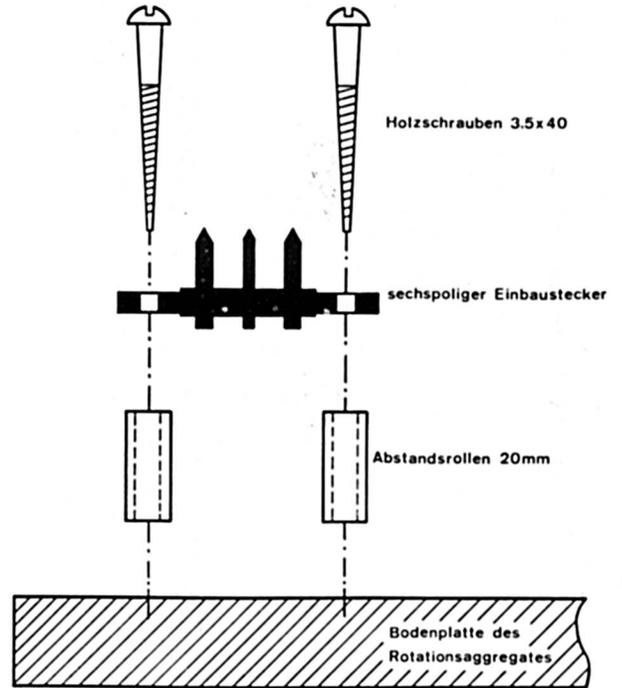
Befestigung des sechspoligen Einbausteckers auf dem Aggregat WR 600
